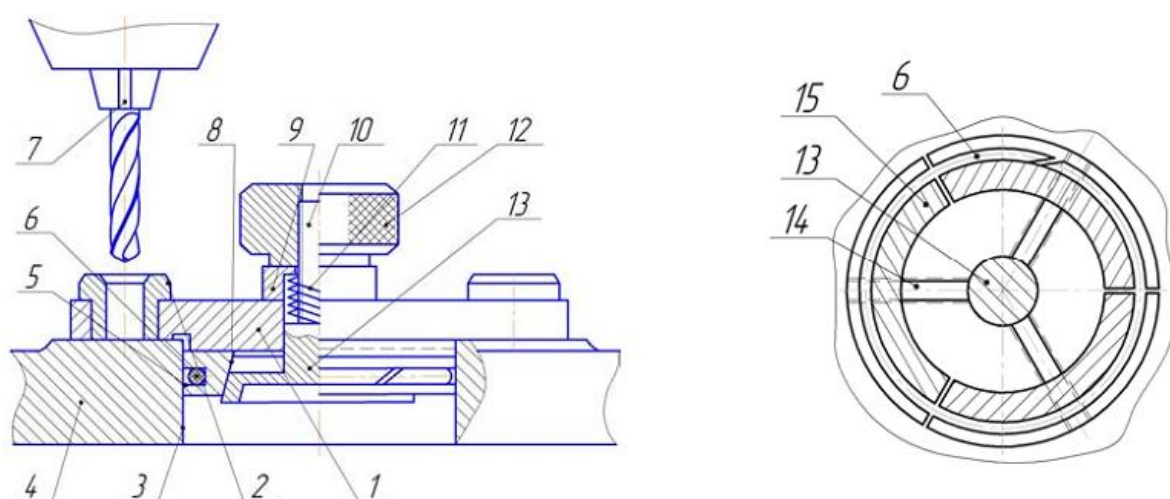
1 – Накладний переналагоджувальний сверлильний кондуктор
